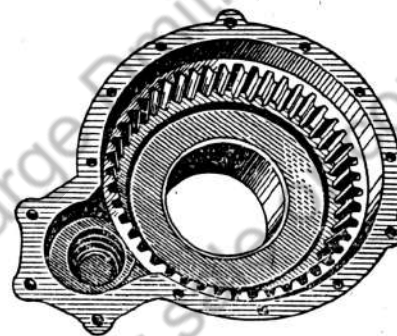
Наружный картер бортовой передачи с неподвижной шестерней.
